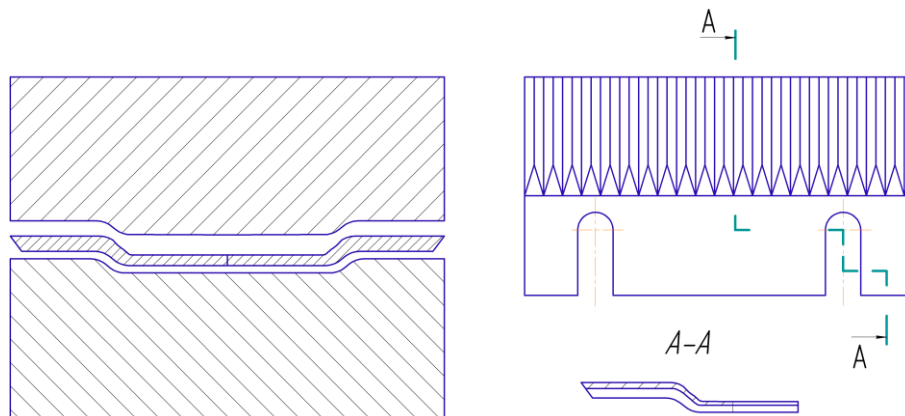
Схема виготовлення заготовок для бурякорізального ножа
